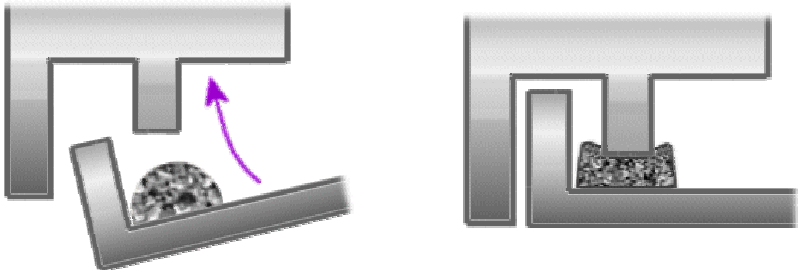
Schaumraupe bei planer Fläche vor und nach dem Verbau
